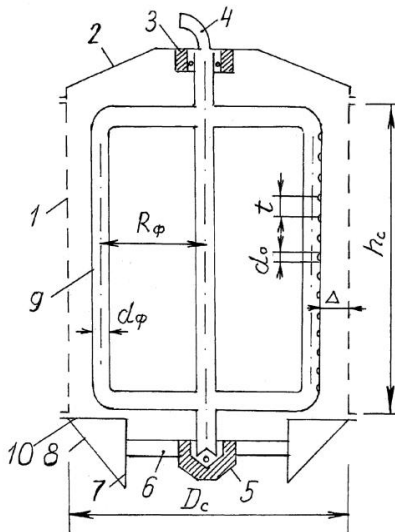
Конструктивна схема ССФ: 1-сітчастий корпус; 2-кришка; 3-верхній (напрямний) підшипник; 4-відвід для підключення промивного рукава; 5-нижній (опорний) підшипник; 6-хрестовина; 7-опорний патрубок; 8-напрямні конструкції для встановлення фільтра на оголовок; 9-флейта; 10-піддон
